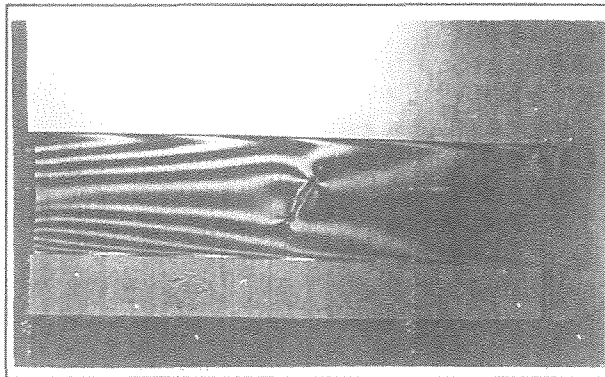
Isocromáticas de soldadura a tope con falta de fusión, sometida a flexión.
